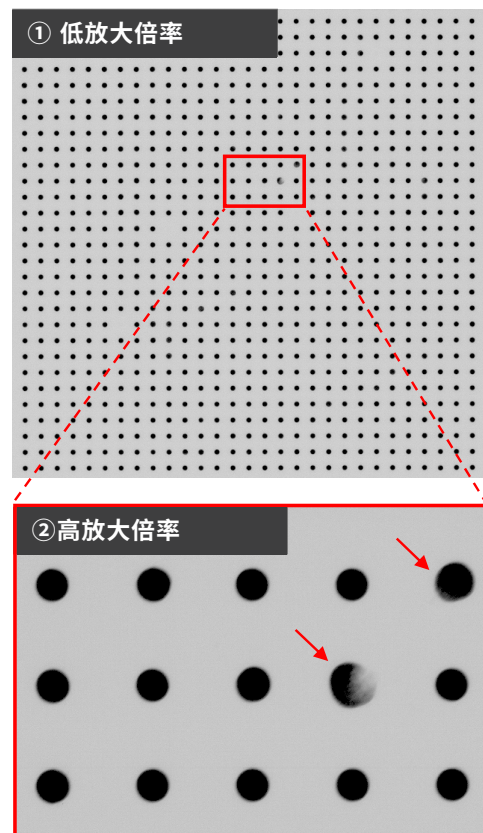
BGA 透视图（红色箭头所指的是缺陷）
